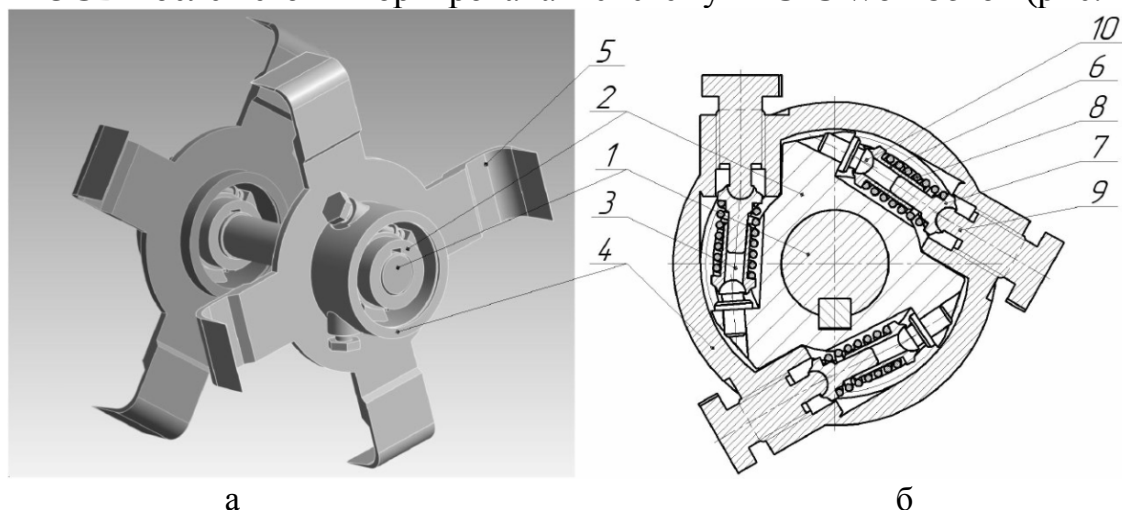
Общий вид 3D-модели вала фрезерной секции, оборудованной демпферными механизмами (а) и схема установки пружин демпфера (б): 1 – вал; 2 – внутренние втулки; 3 – блок пружин; 4 – наружная втулка; 5 – диски фрез с Г-образными ножами; 6, 7 – втулки направляющие; 8 – пружина; 9, 10 – сферические опоры
